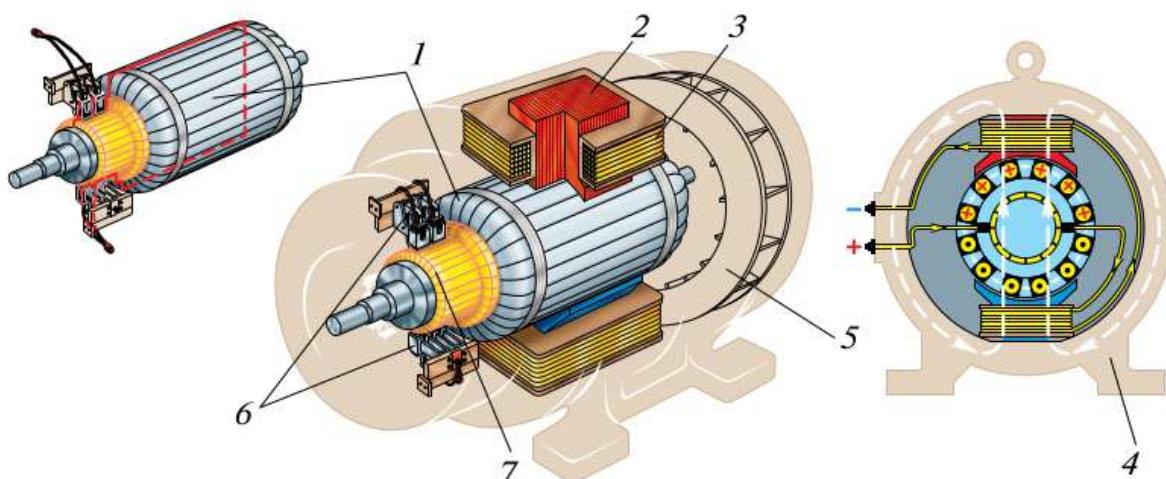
Схема коллекторного двигателя: 1 — ротор; 2 — сердечник полюса; 3 — обмотка полюса; 4 — статор; 5 — вентилятор; 6 — щётки; 7 — коллектор
